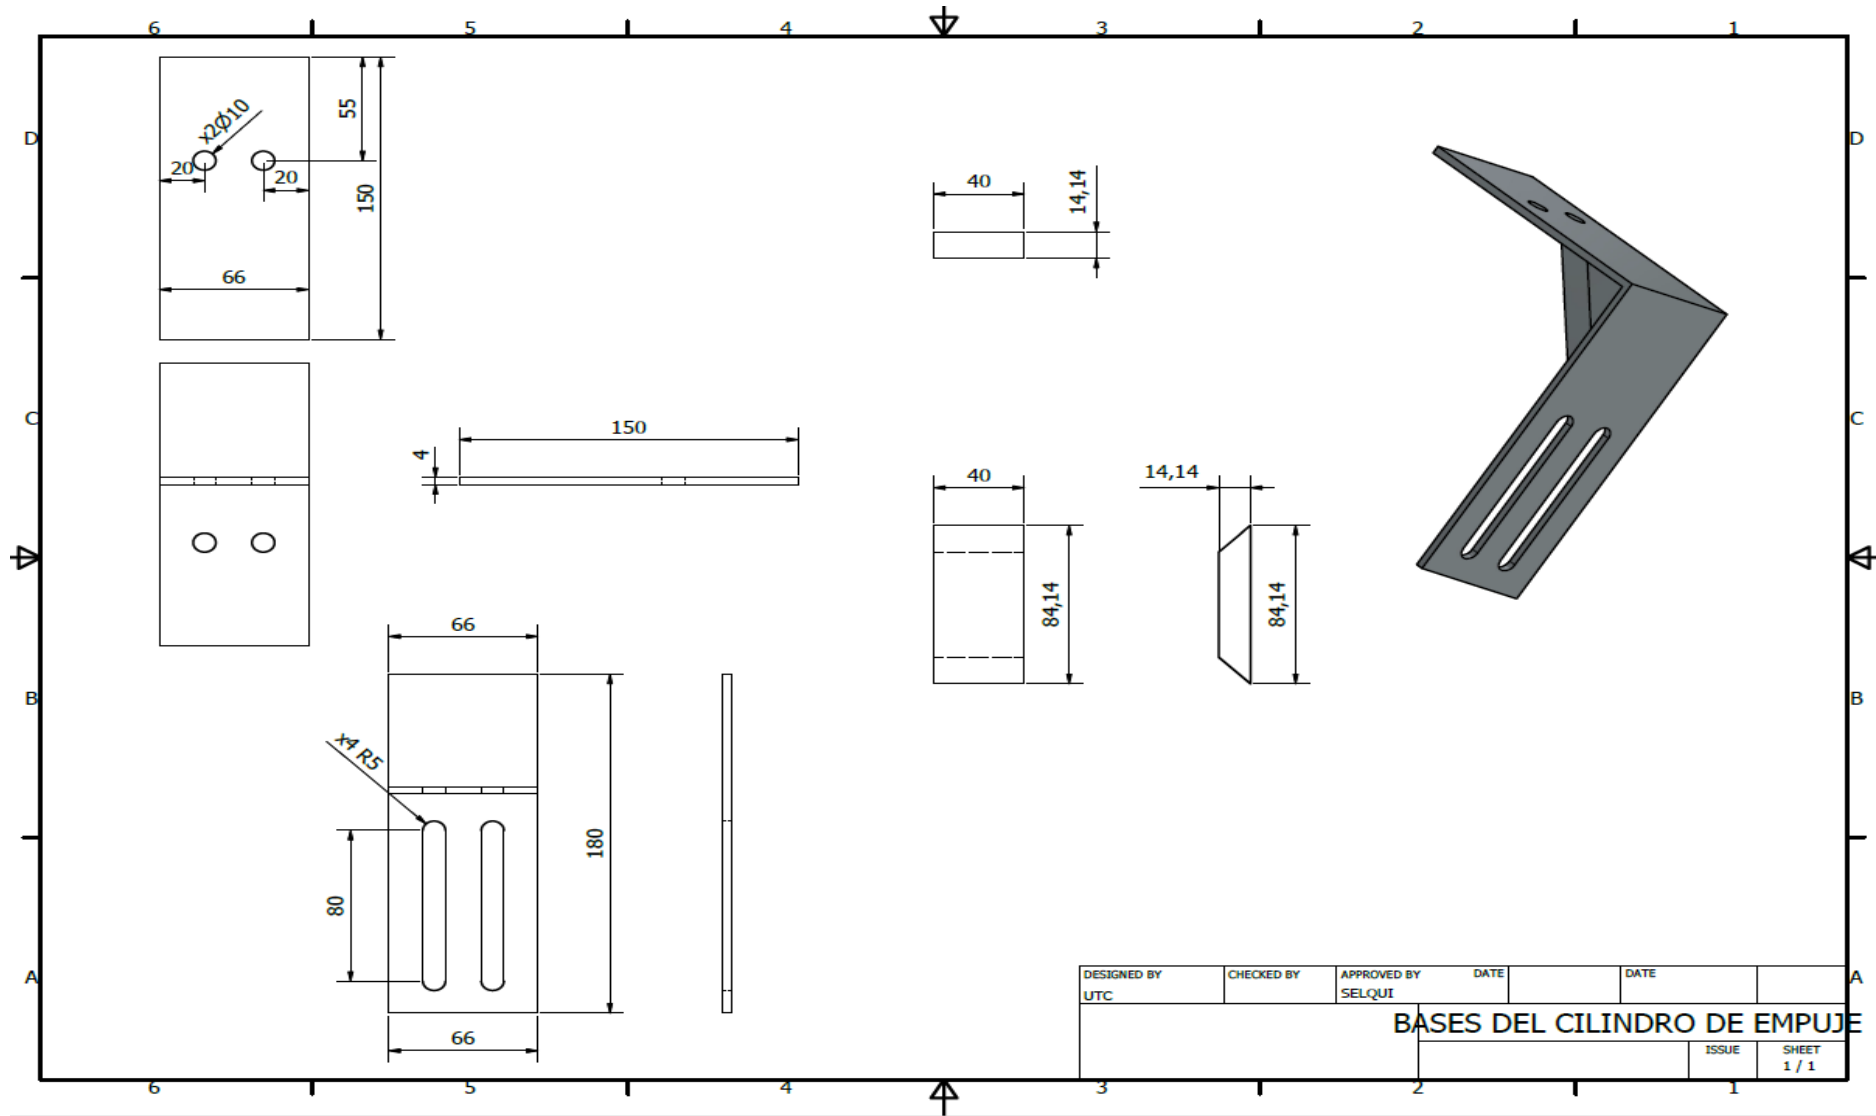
Plano de acoplamiento para el cilindro de empuje
